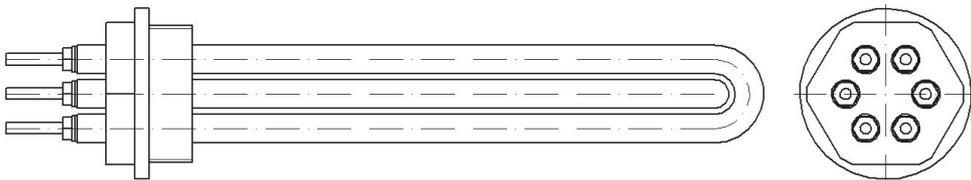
Трубчатый электронагреватель блочный (ТЭНБ).
